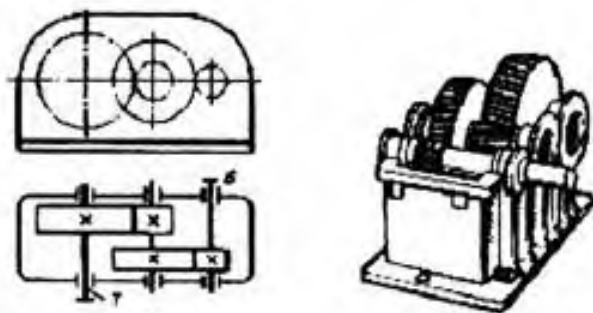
Двоступінчатий циліндричний горизонтальний редуктор
